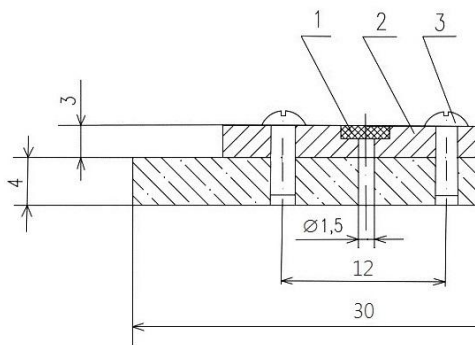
Пристрій для вимірювання поверхневого електричного опору зразка композита: 1 – зразок композита; 2 – пластина з фторопласта; 3 – гвинт з різьбою M2,0; 4 – підставка з нержавіючої хромонікелевої сталі 14X17H2.
